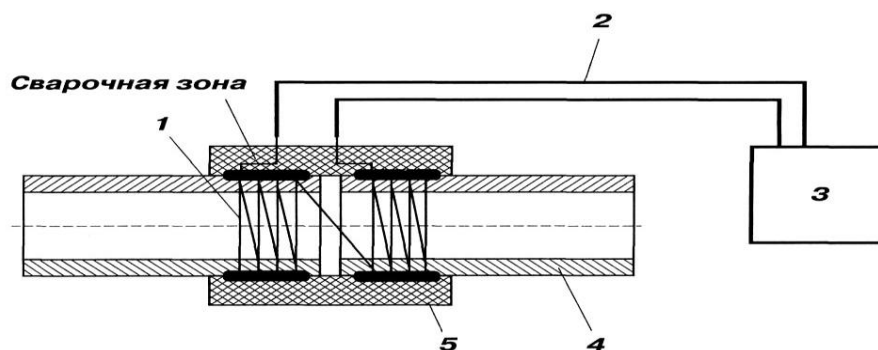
Принципиальная схема электромуфтовой сварки:
